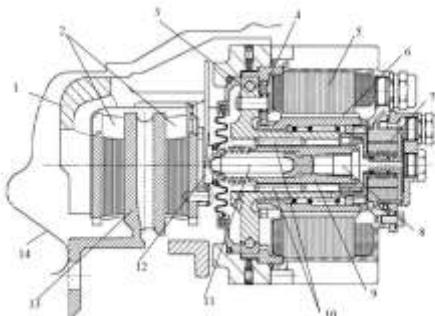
Конструкція виконуючого елемента; 1 – супорт; 2 – гальмівні колодки; 3 – центральний підшипник; 4 – планетарний механізм; 5 – статор; 6 – ротор/гайка; 7 – вирішальний пристрій; 8 – датчик сили; 9 – шпиндель; 10 – планетарні ролики; 11 – натискний шток; 12 – підтримка колодки; 13 – гальмівний диск; 14 – корпус.
